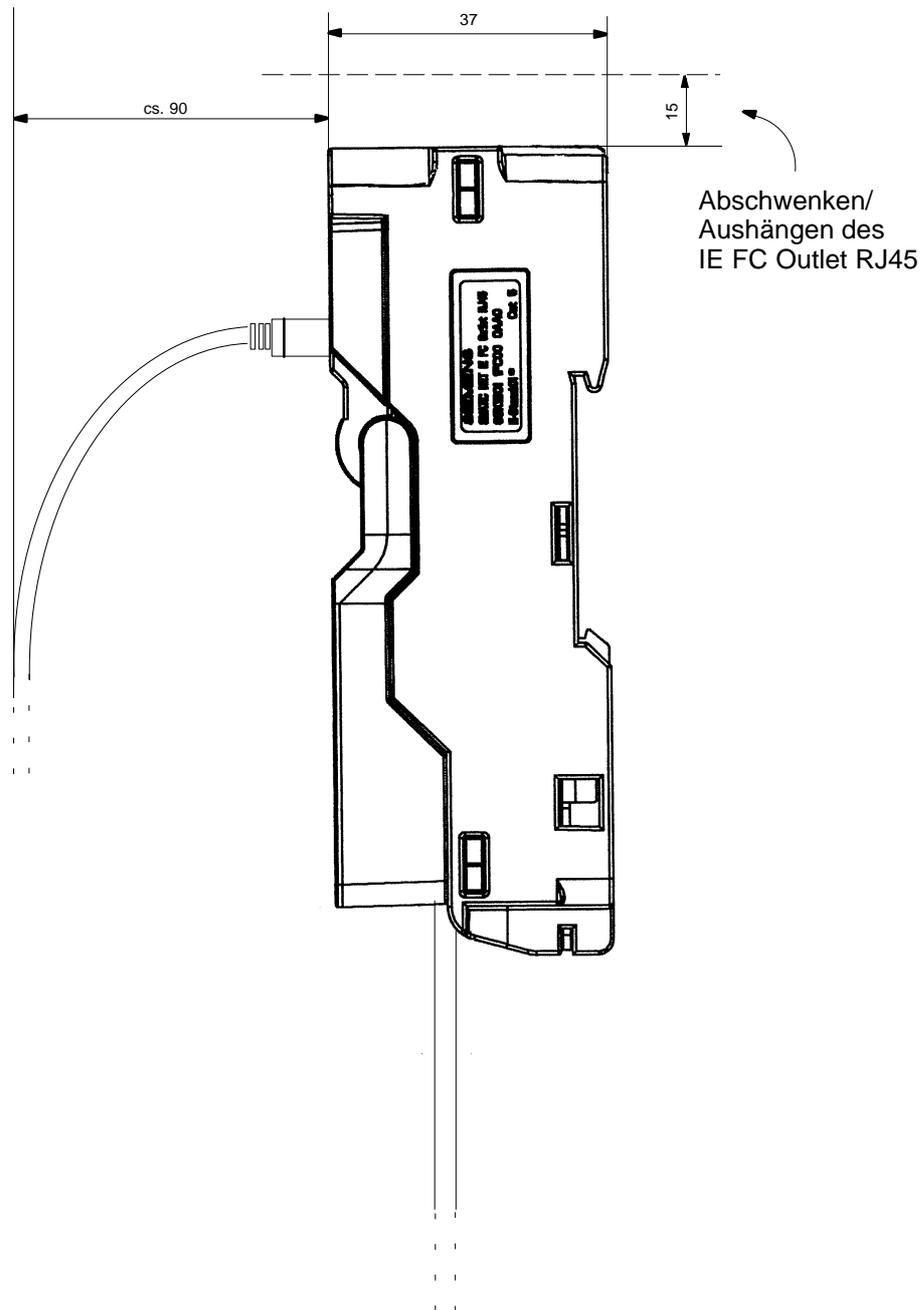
IE FC Outlet RJ45 (Maße in mm)
